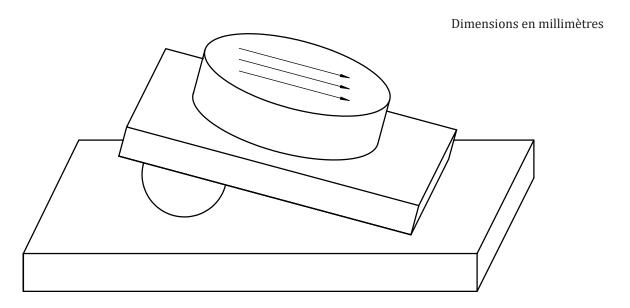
Exemple de verre plan incliné et de plan de mesure
